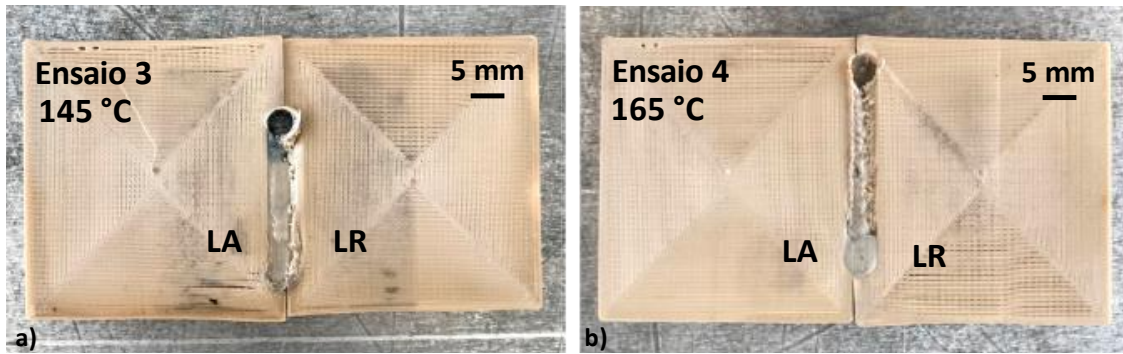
Aspeto visual da superfície das placas soldadas de PEEK: a) Ensaio 3, b) Ensaio 4.
